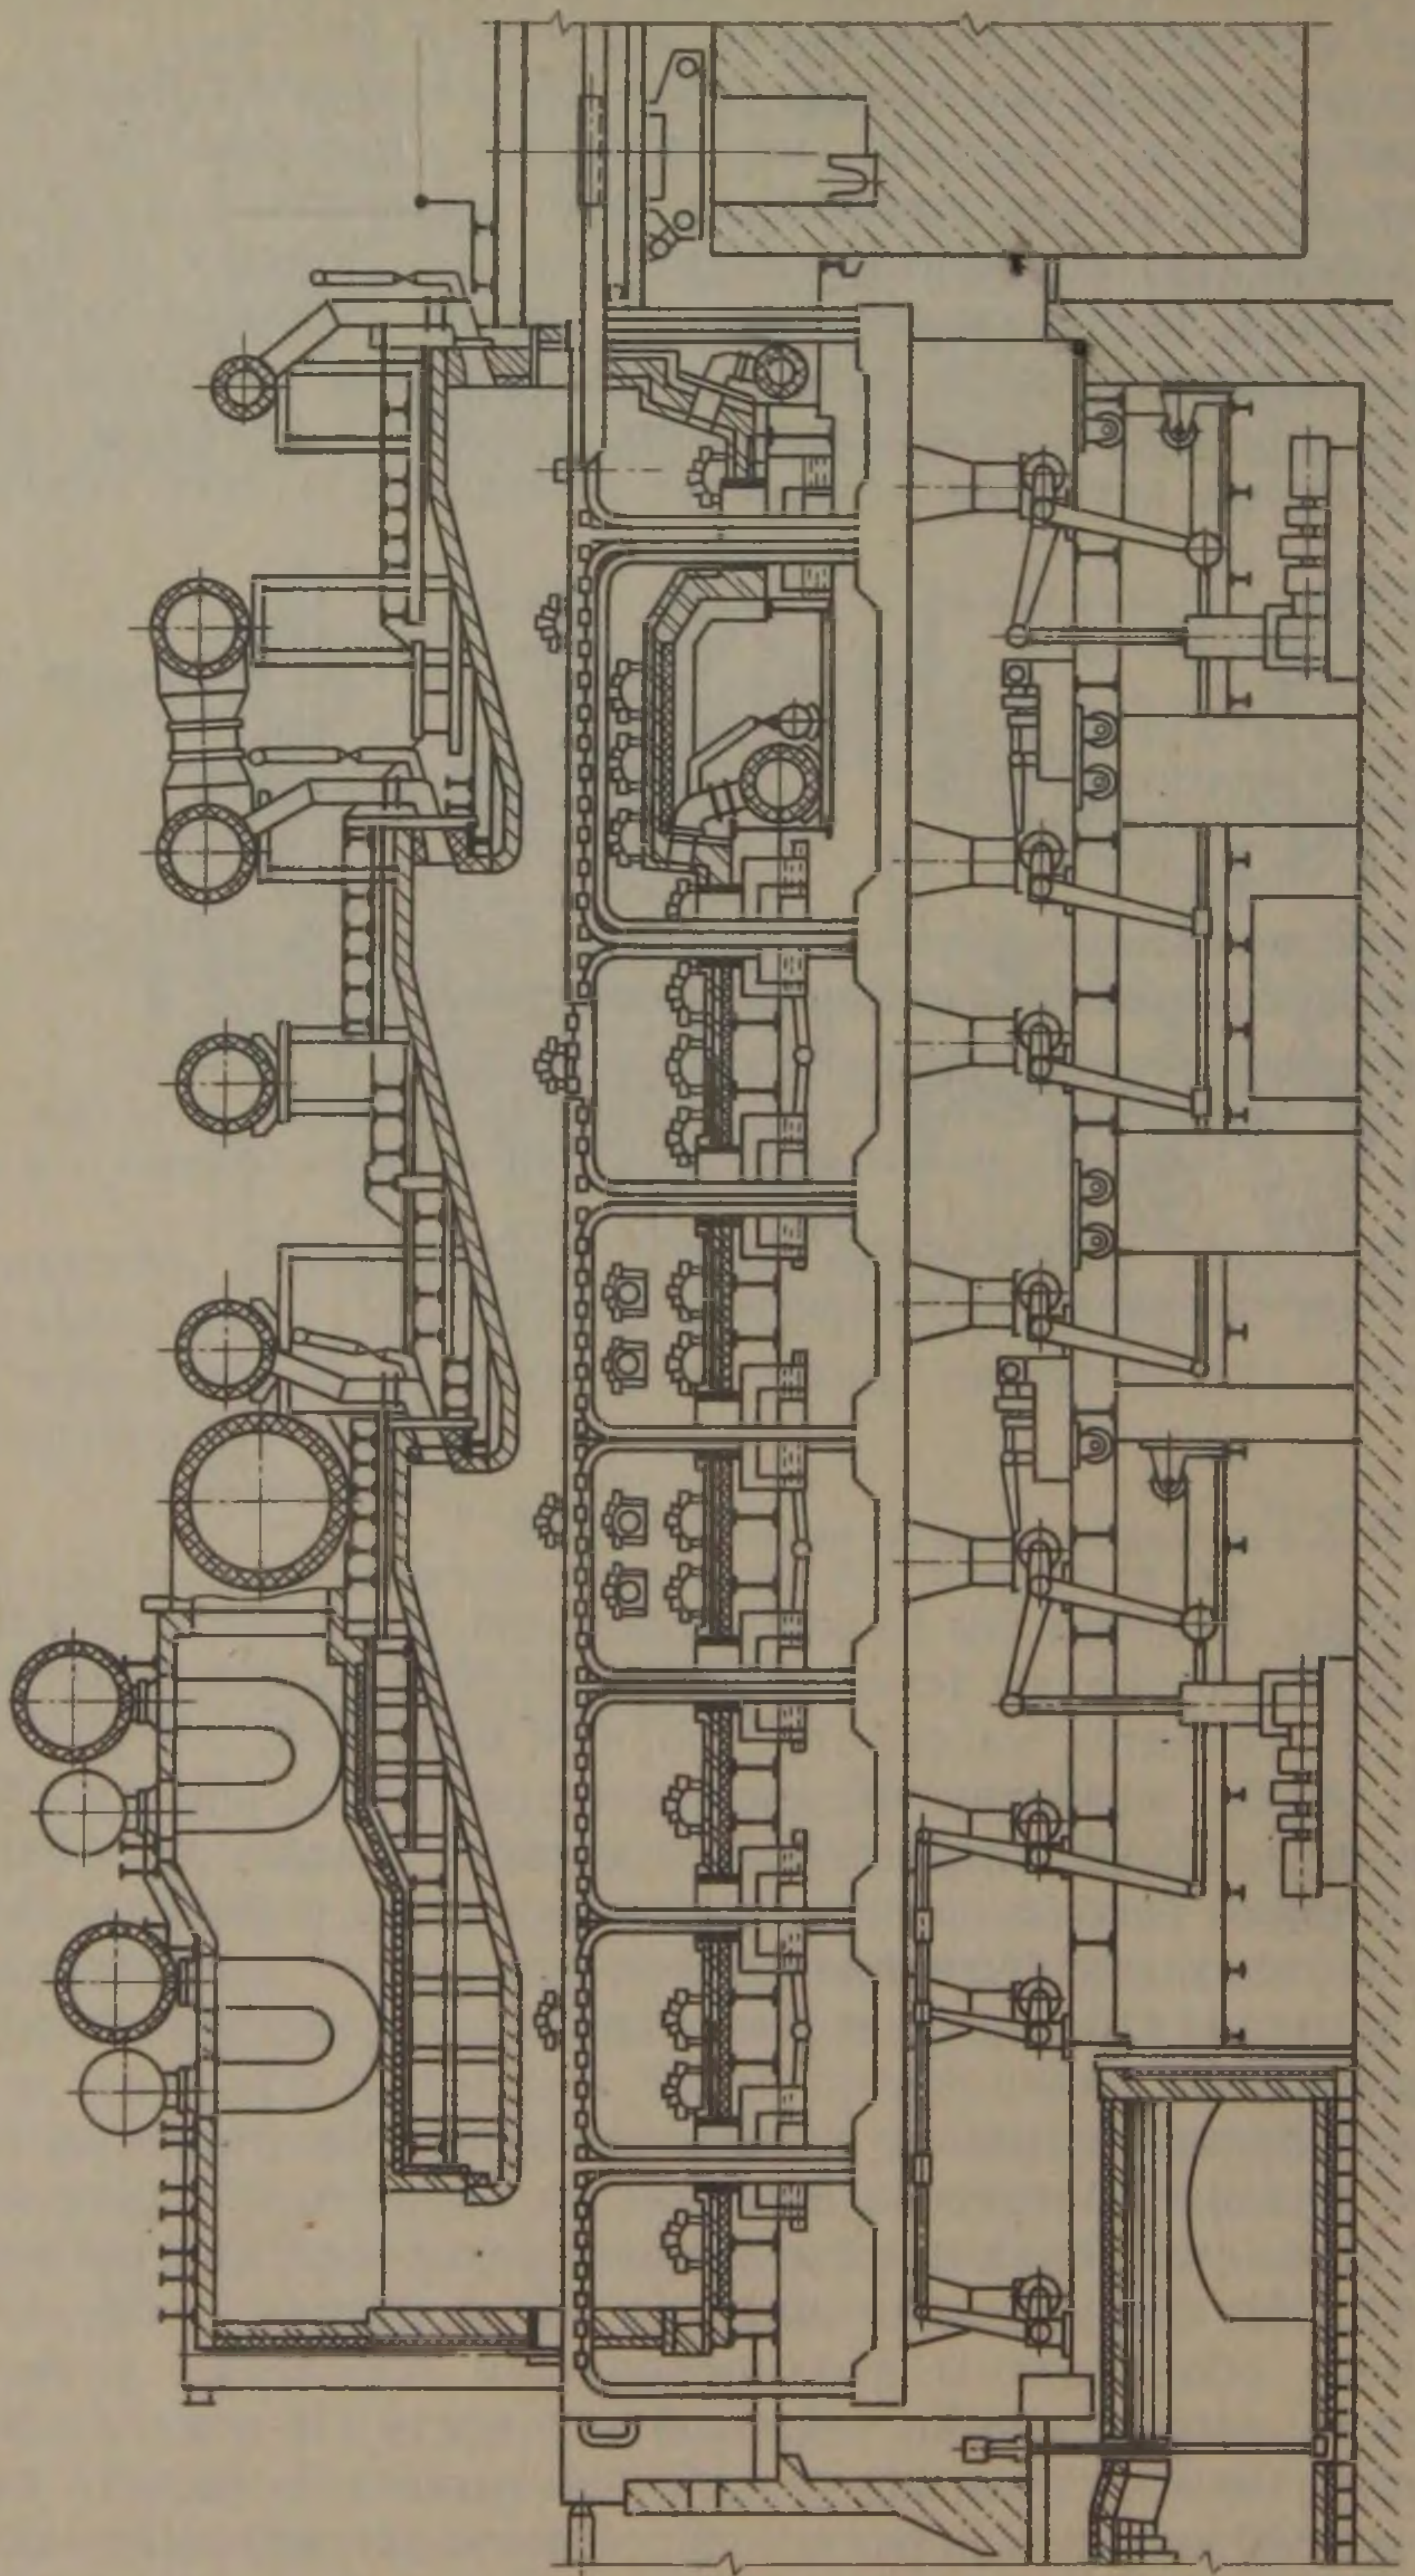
Печь с шпательными балками с нижним обогревом металла
